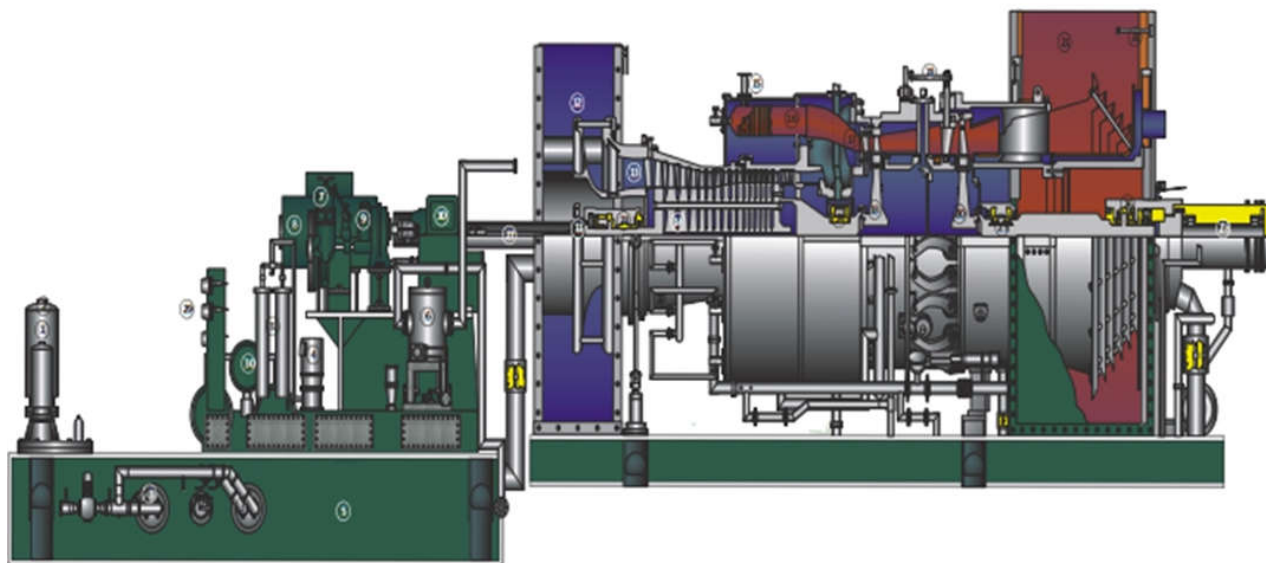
Газоперекачувальний агрегат ГТК-25И
